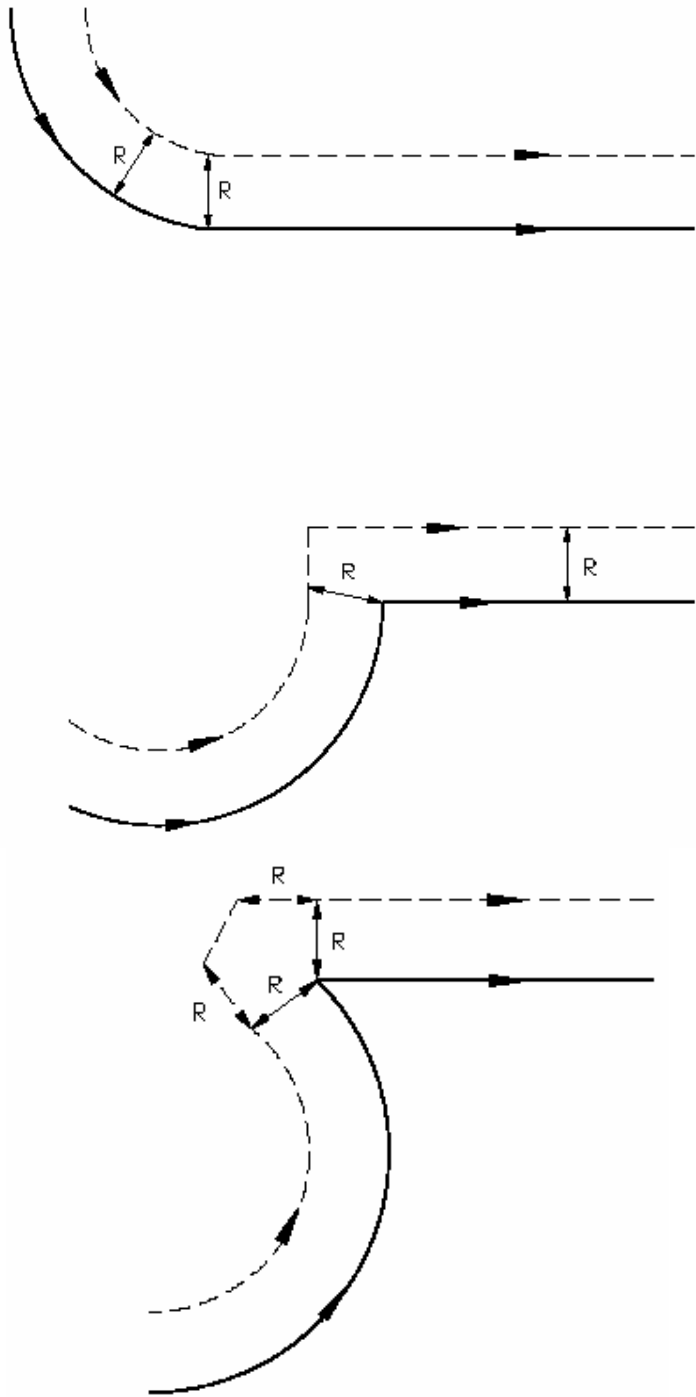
27 (4) 刀具半径补偿的刀具轨迹
